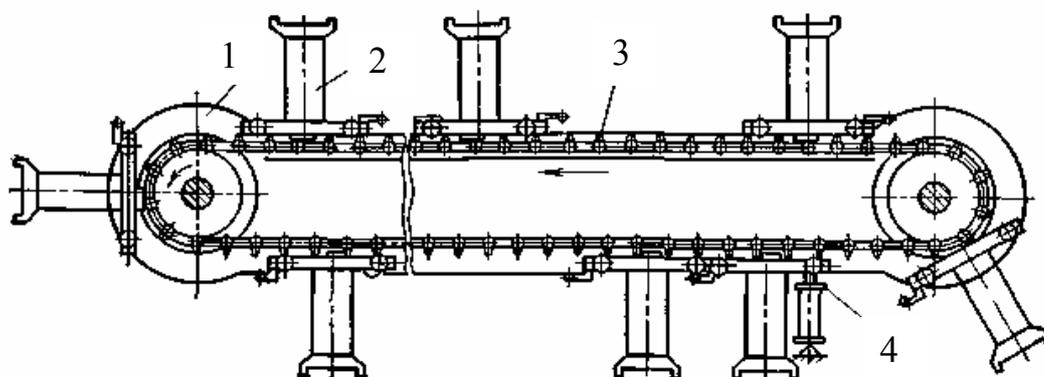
Тележечный конвейер для сборки агрегатов: 1 – направляющие; 2 – грузонесущая тележка; 3 – тяговая цепь; 4 – останов
